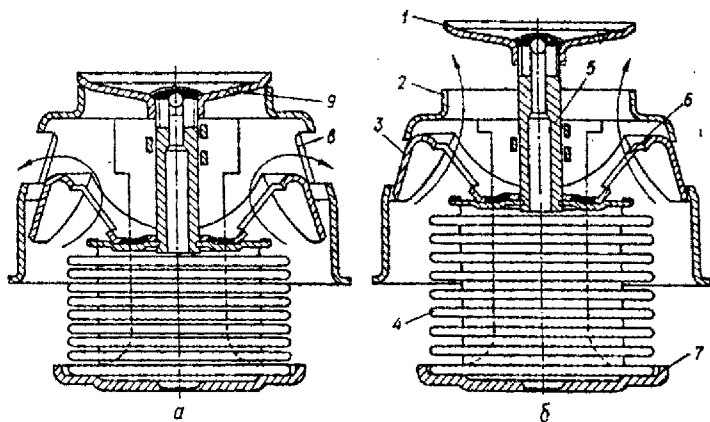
Устройство и работа термостата с жидким наполнителем: а – главный клапан закрыт; б – главный клапан открыт; 1 и 3 – вспомогательный и главный клапаны; 2 – корпус; 4 – гофрированный цилиндр; 5 – шток; 6 и 8 – окна в клапане и корпусе; 7 – скобка; 9 – отверстие для выхода воздуха
